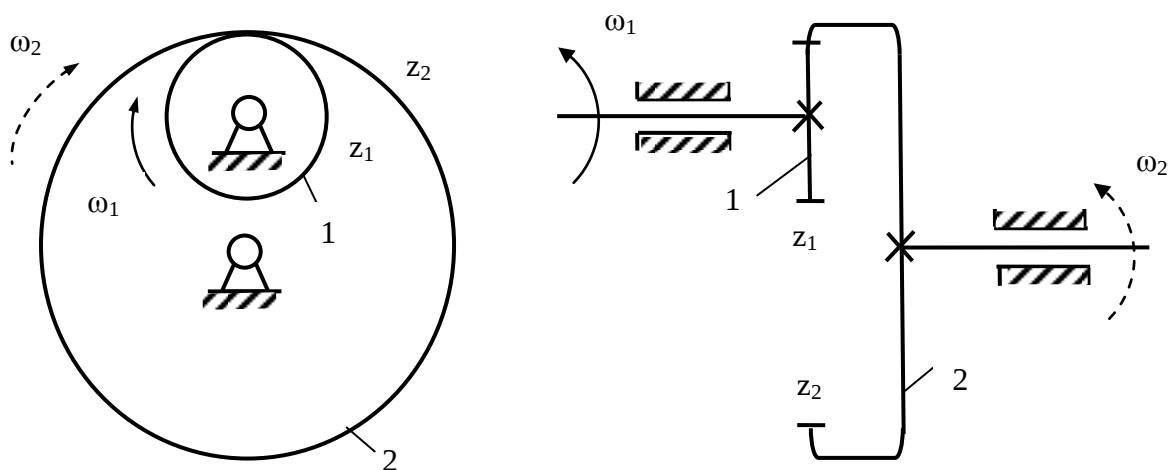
Схема одноступенчатой цилиндрической прямозубой передачи внутреннего зацепления
